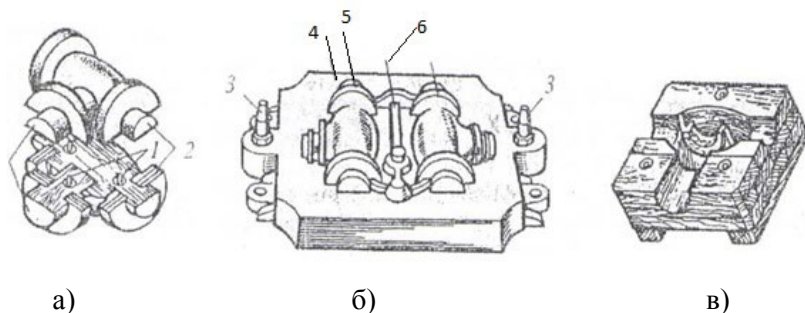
Литейная модель (а), модельная плита (б) и стержневой ящик (в) для корпуса вентиля: 1 - центрирующие шипы; 2 - стержневые знаки; 3 - центрирующие штыри; 4 - металлическая плита; 5 - модели отливок; 6 - модели элементов литниковой системы
